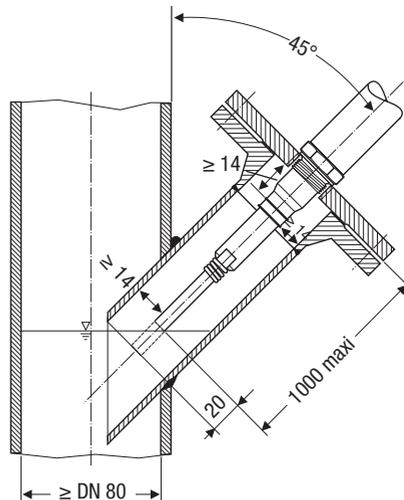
Montage en position inclinée, par ex. dans les conduites de départ montantes d'installations à eau surchauffée ou dans des réservoirs
